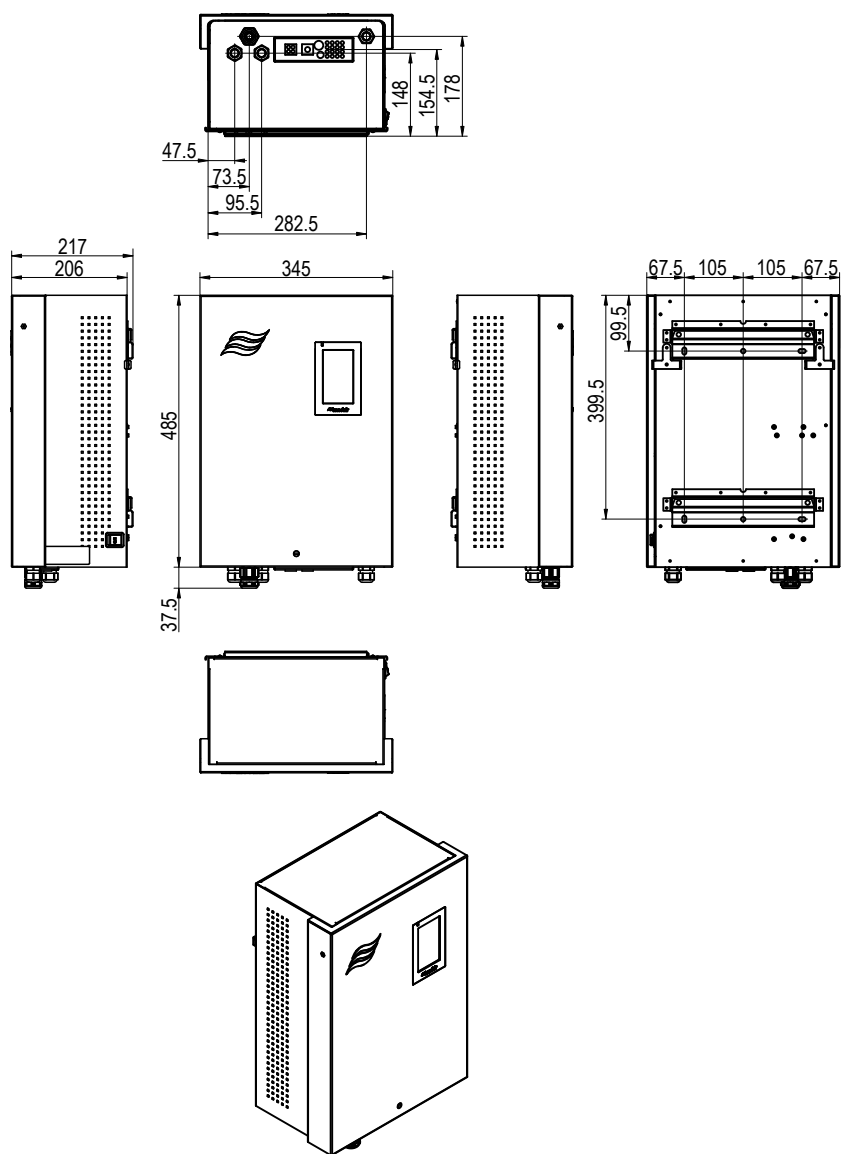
Esquema de dimensiones de la unidad de control (dimensiones en mm)
